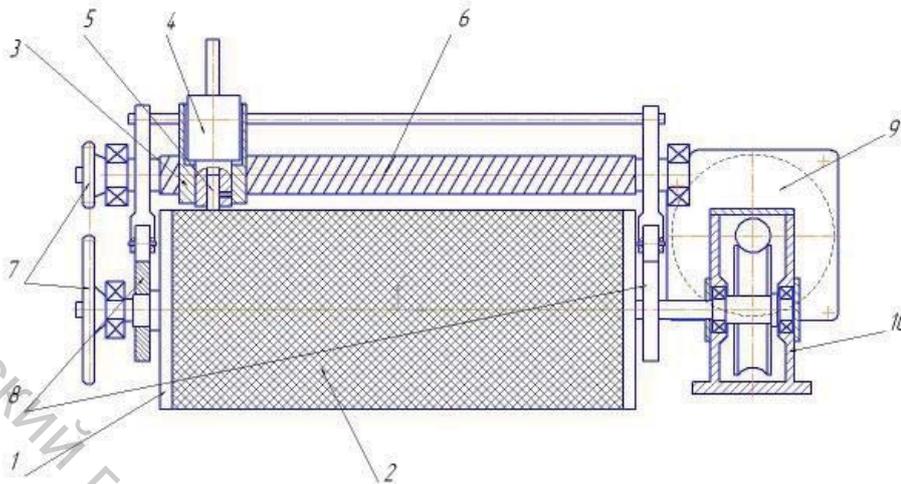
Схема установки для испытания пластмасс на абразивный износ по методу Шоппера
